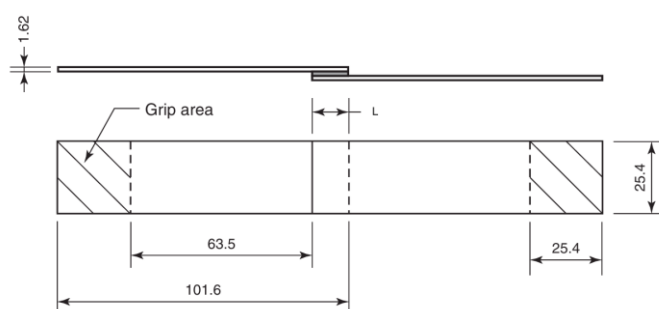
Dimensões do corpo de prova de juntas adesivas com dimensões em milímetros.
